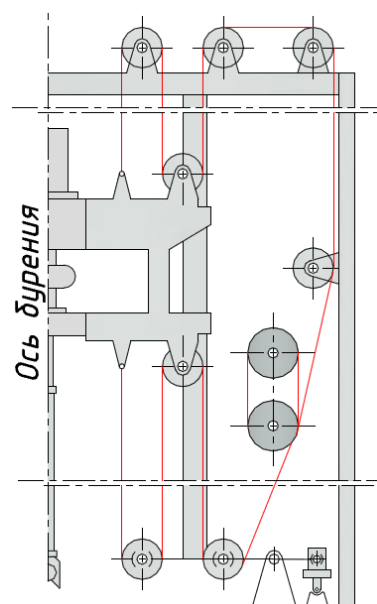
Принципиальная кинематическая схема вращательно – подающего механизма станка СБШС – 250/270-32.
